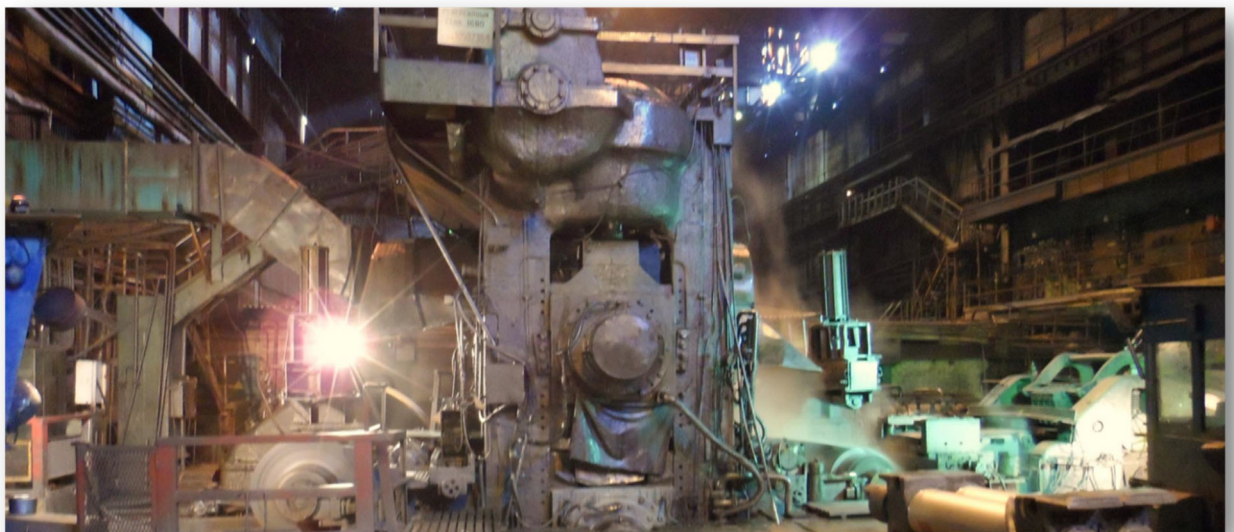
Реверсивний стан холодної прокатки 1680 ПАТ «Запоріжсталь»
